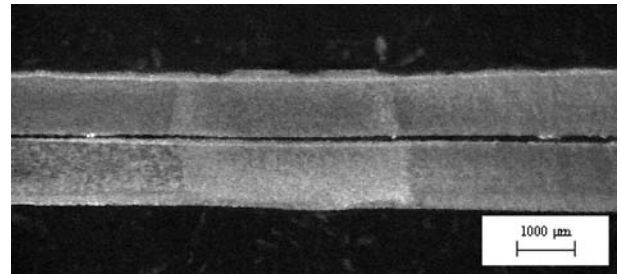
Macrografía de la sección transversal de una falta de soldadura.
